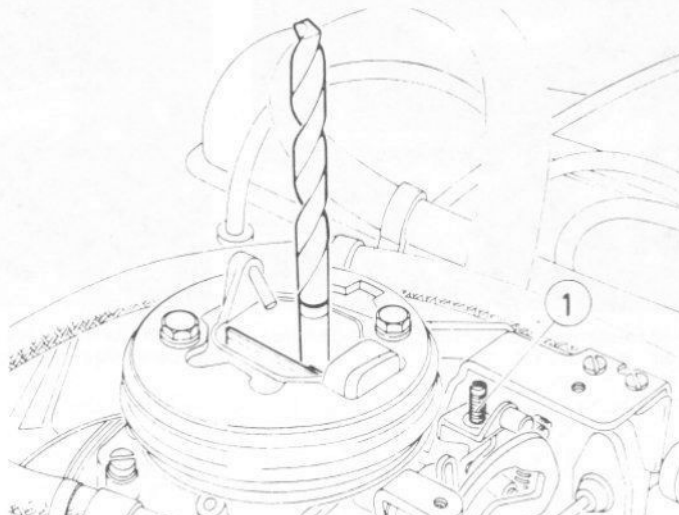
Vis de réglage de l'OVAD (1) - carburateur Weber 36 TLC (Sec 8)
